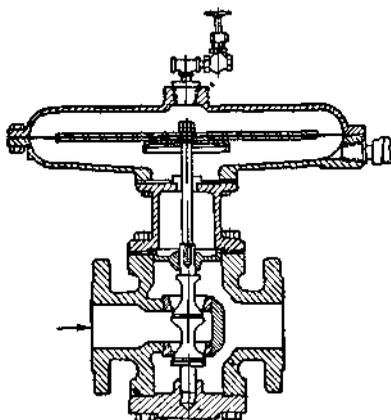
Устройство пневматического исполнительного механизма без пружины
